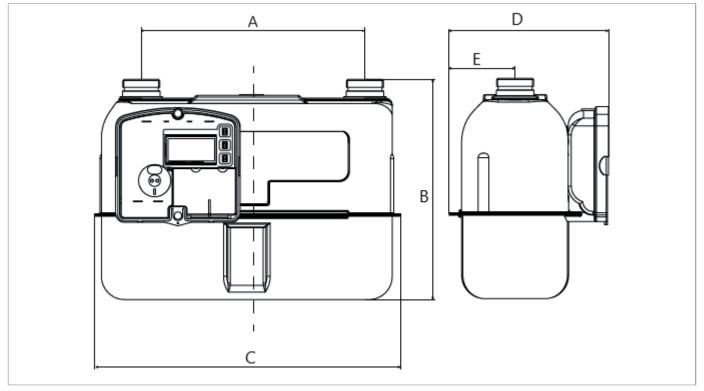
Dimensiones RSE - RSV (2.4 LA)
